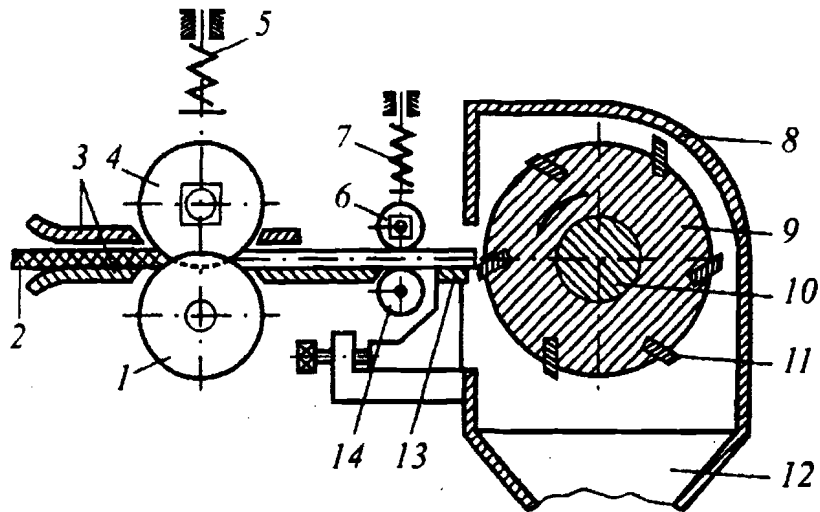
Схема дробилки с дисковыми ножами и режущим ротором («дайсер»):
